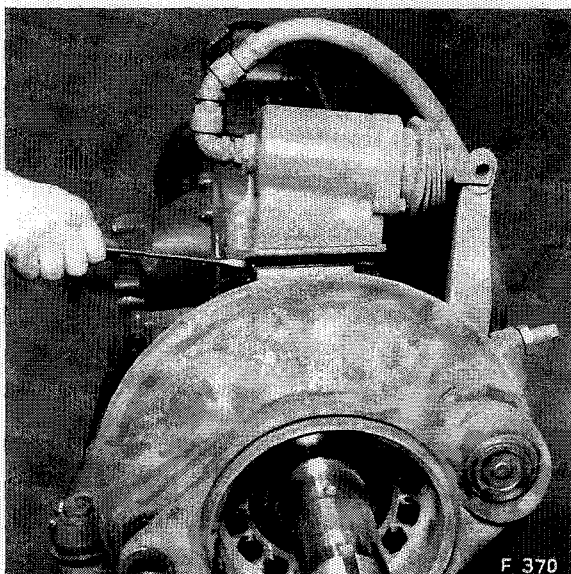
Lösen der Befestigungsmuttern für den Bremszylinder
